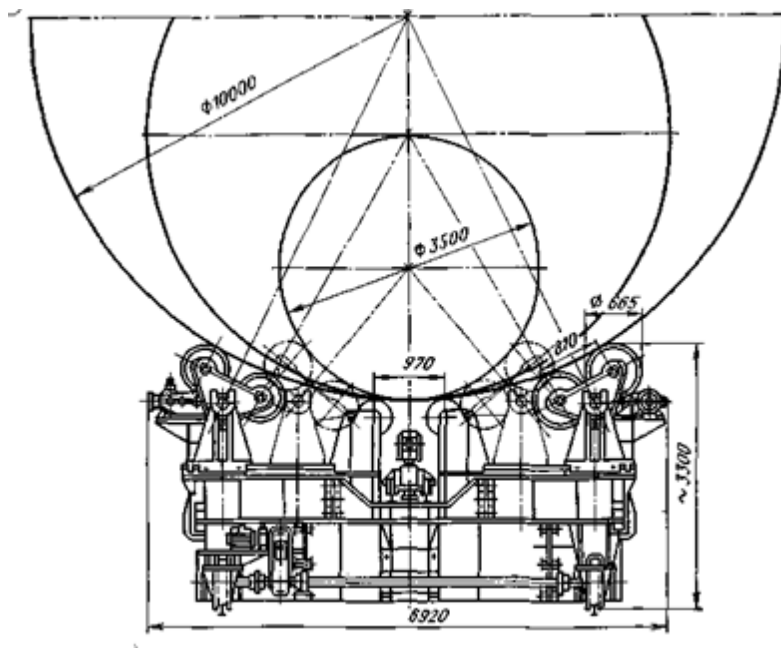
Схема роликового стенда для базування деталей циліндричної форми
